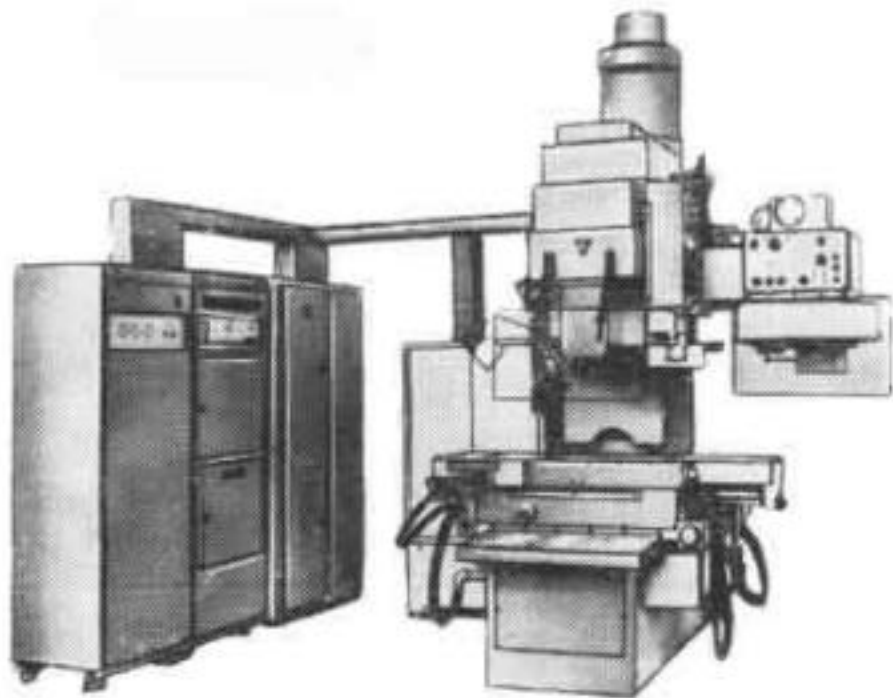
Загальний вигляд вертикально – фрезерного верстату
